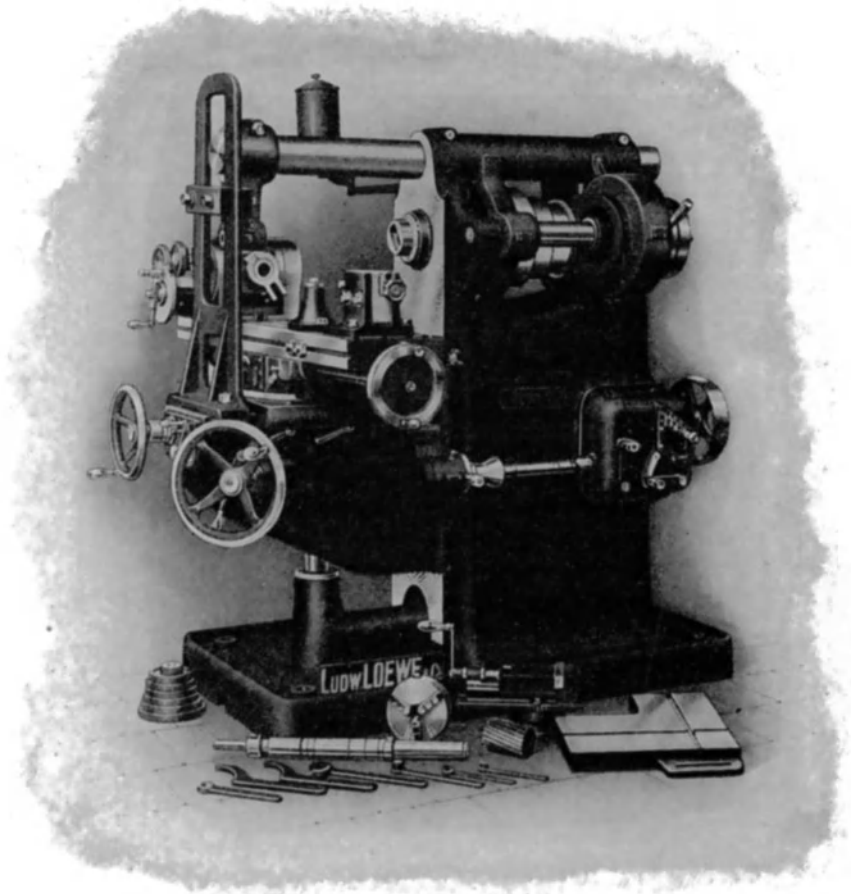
Die Universalfräsmaschine von L. Löwe & Co.
